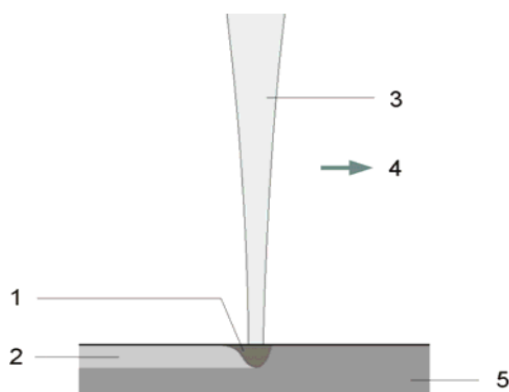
Representação esquemática dos diferentes tipos de soldadura laser [12]
